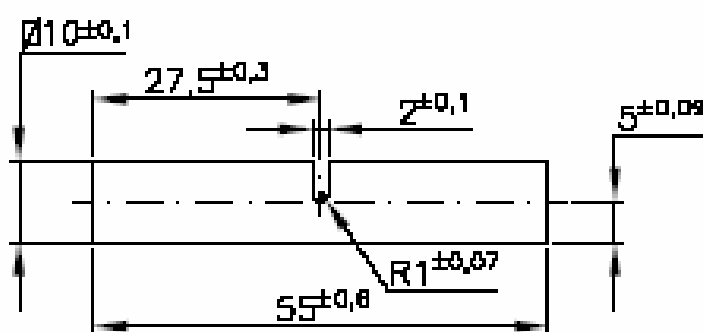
Dimensões dos corpos de prova para ensaios Charpy – Impacto
